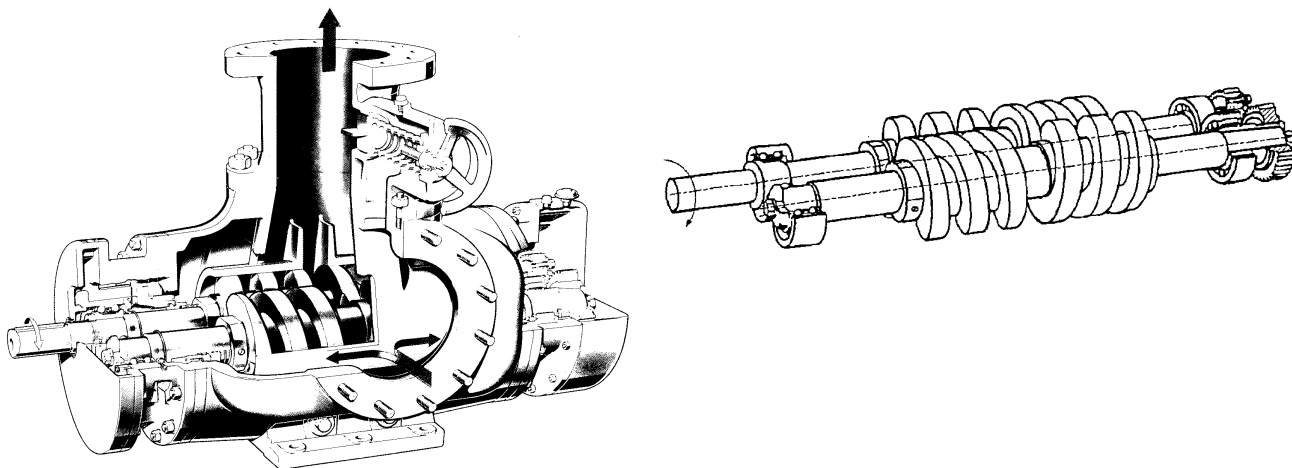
b.- Bomba de tornillo doble; vista de conjunto
